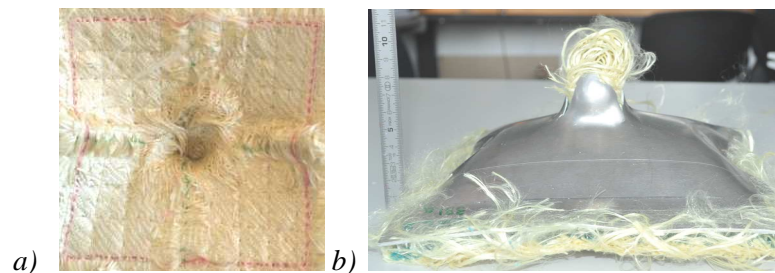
Echantillon après impact – Cas 2C : a) face avant; b) face arrière
